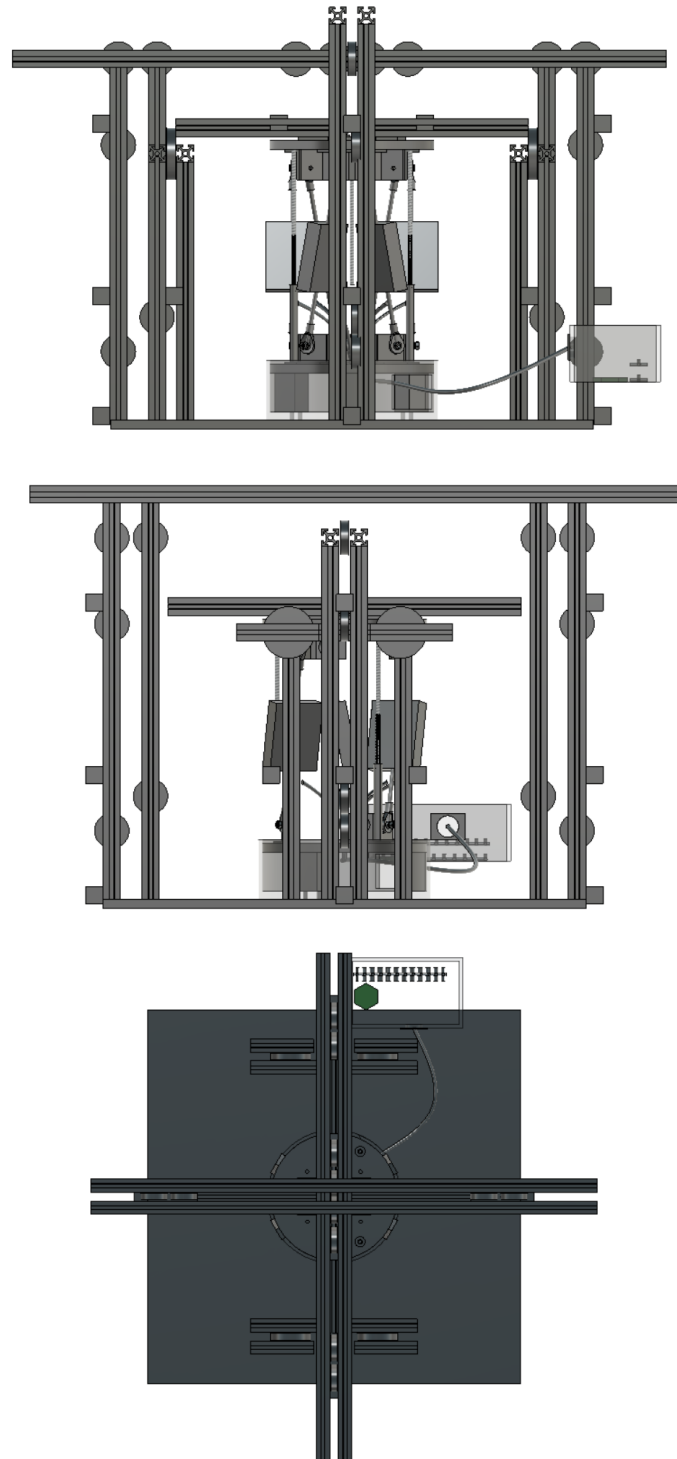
Montaje sistema de calibración balanza túnel de viento: alzado, perfil y planta
